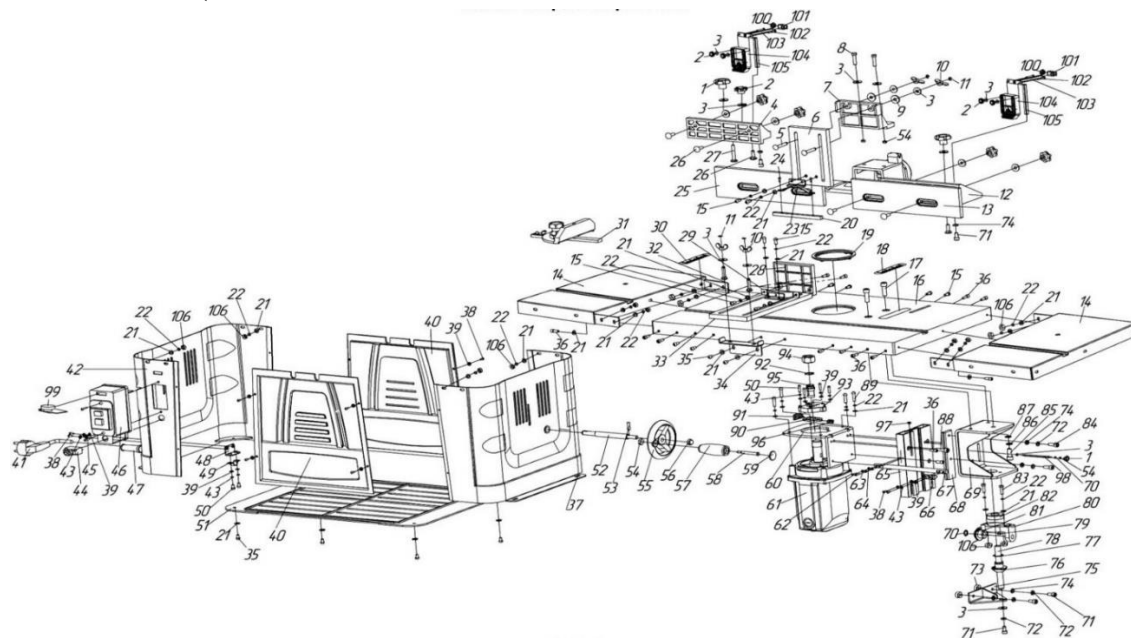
Детальная схема состава фрезерного станка Корвет-82
